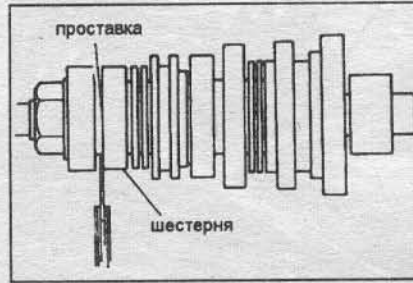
г Измерения осевого зазора шестерни 4-й передачи.
